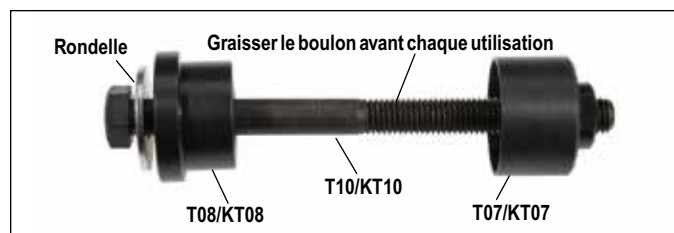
OUTIL DE FIXATION DU CACHE-POUSSIÈRE DE LA COURTE TIGE DE GUIDAGE
